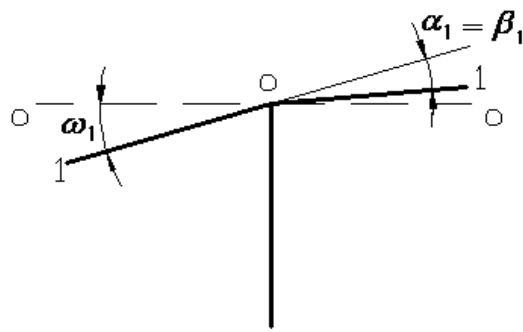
Distorsión angular producida por la ejecución del primer cordón de soldadura
